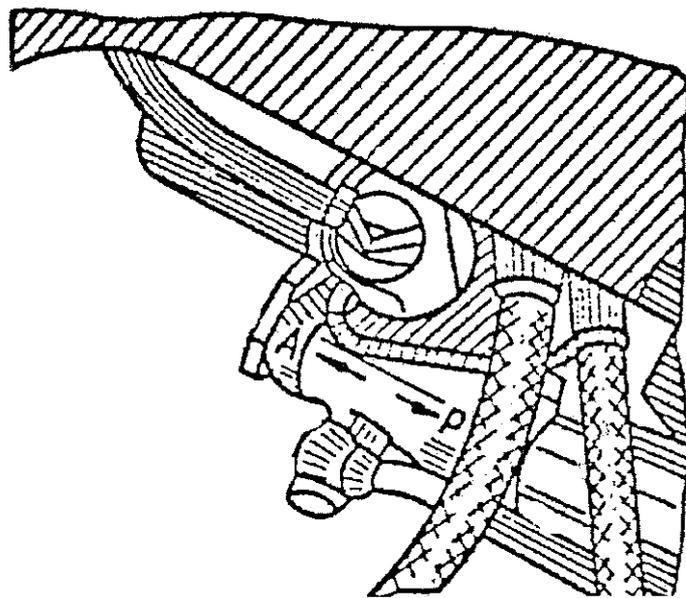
Установка рукоятки золотниковой коробки
